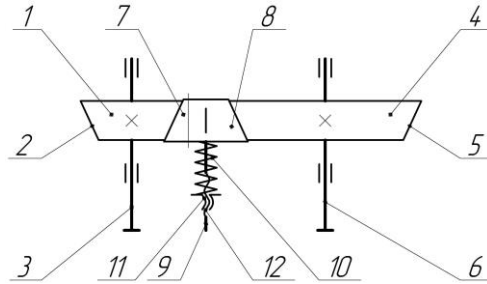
Кінематична схема фрикційної передачі: 1 – ведучий коток; 2, 5, 8 – конічні робочі поверхні; 3 – ведучий вал; 4 – ведений коток; 6 – ведений вал; 7 – проміжний вал; 9 – вісь; 10 – циліндрична пружина стиску; 11 – гайка; 12 – різьба
